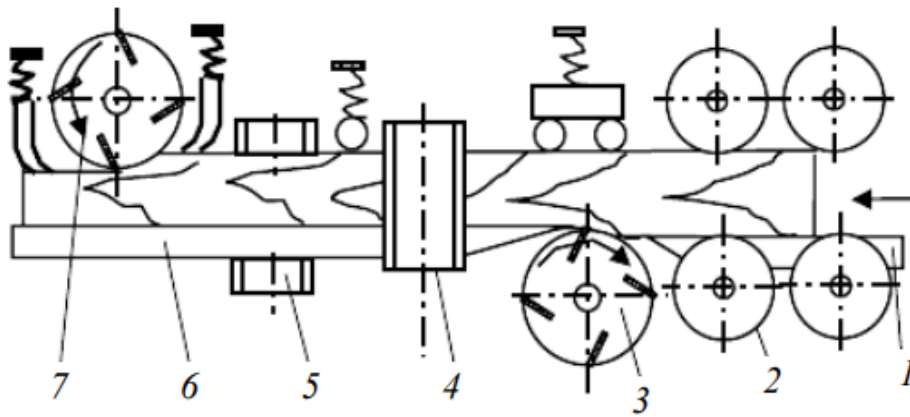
Схема пристрою чотиристороннього поздовжньо-фрезерного верстата
